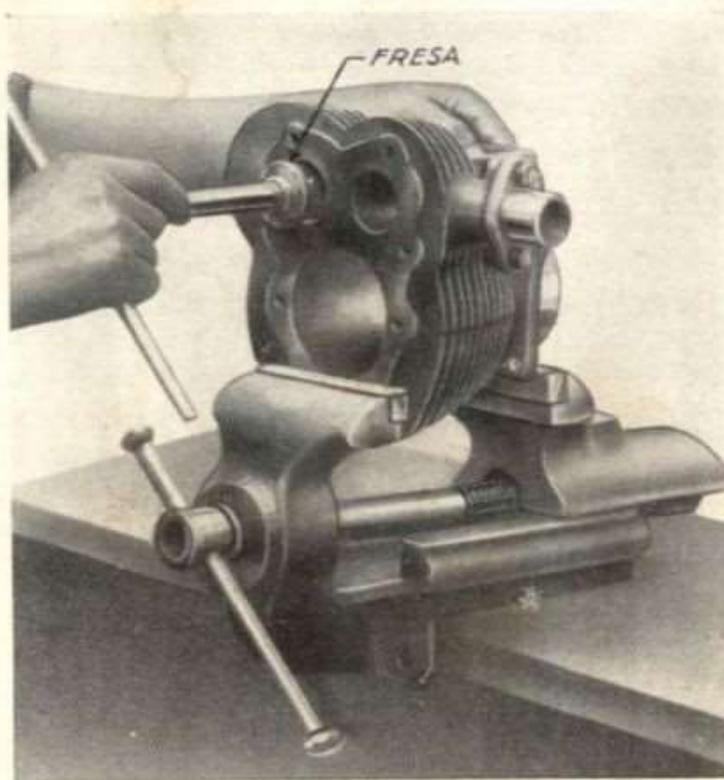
A 15 Utensile a forma di fresa per ripassatura sedi valvole
